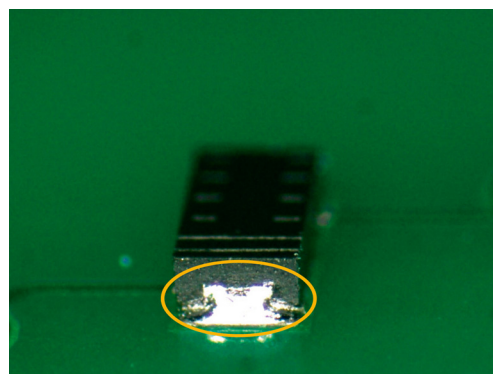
焊接后的可湿性侧面(DFN1608)外观
